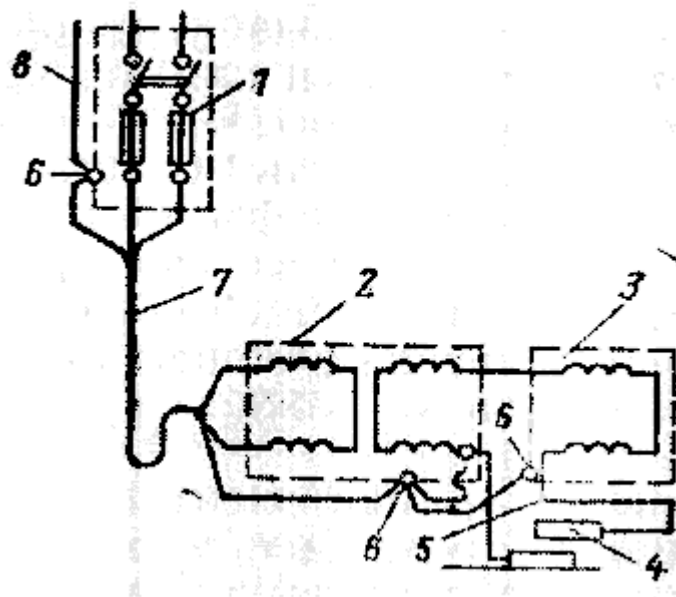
Схема подключения сварочного трансформатора:
